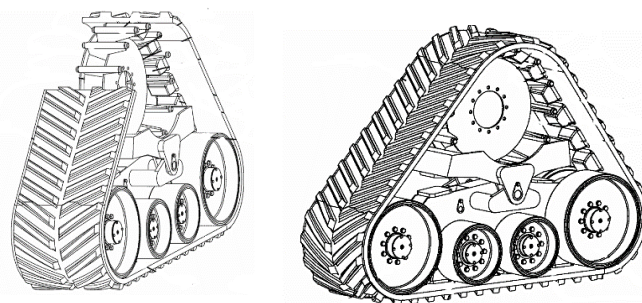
Внешний вид конструкции патента RU 2591782
